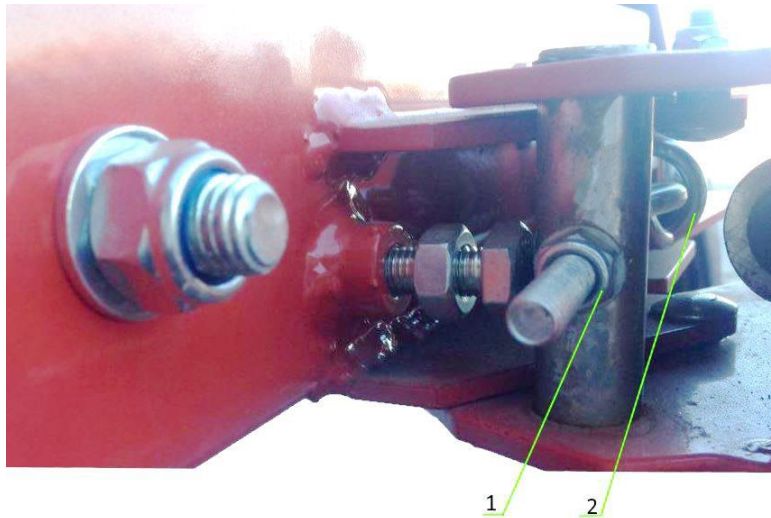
Регулировка натяжения пружины в предохранительном рычаге:
